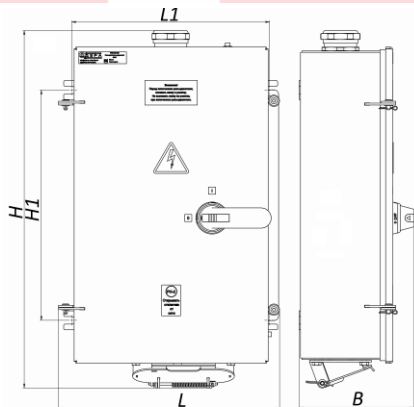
Общий вид и габаритные размеры ССН-Ш-В
